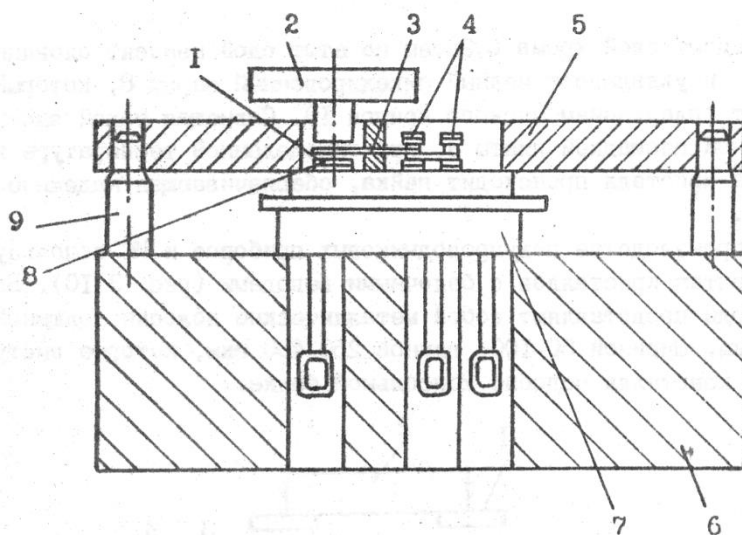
Схема сборки транзисторов в прецизионной кассете: 1 – кристалл; 2 – грузик; 3 – паз для ориентации вывода; 4 – навеска из припоя; 5 – трафарет; 6 – корпус кассеты; 7 – ножка транзистора; 8 – прокладка из припоя; 9 – направляющие
